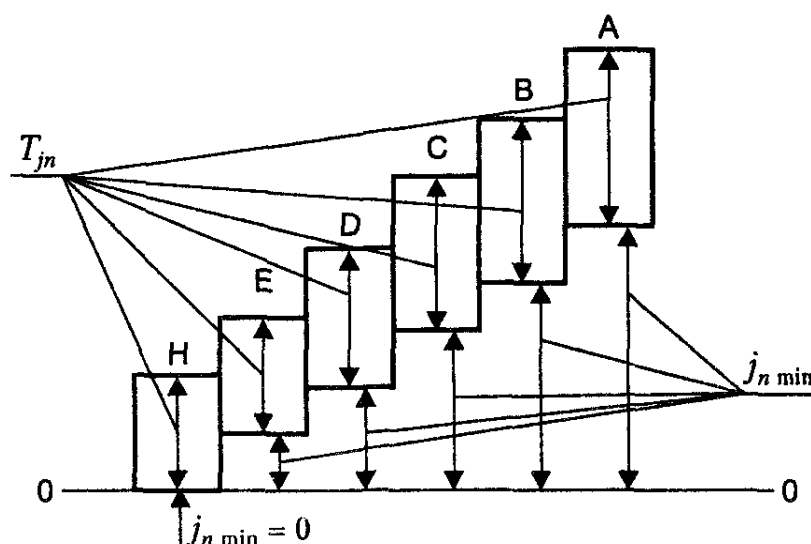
Виды сопряжений и допуски на боковой зазор
